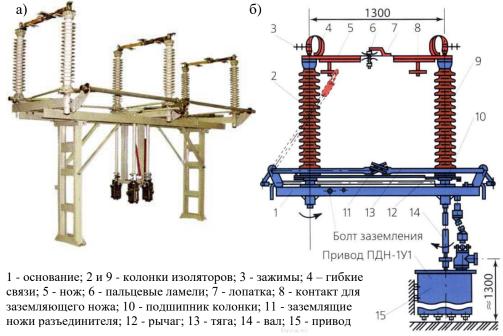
Внешний вид (a) и конструкция (б) трехполюсного разъединителя типа РНДЗ
